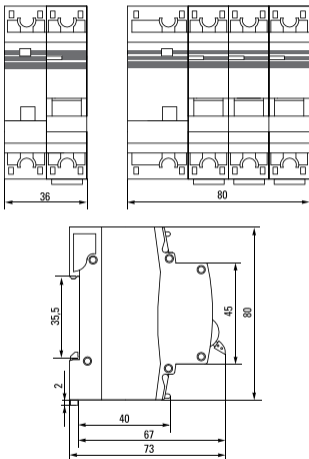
Габаритные и установочные размеры АД-32 - двухполюсный и четырехполюсный
